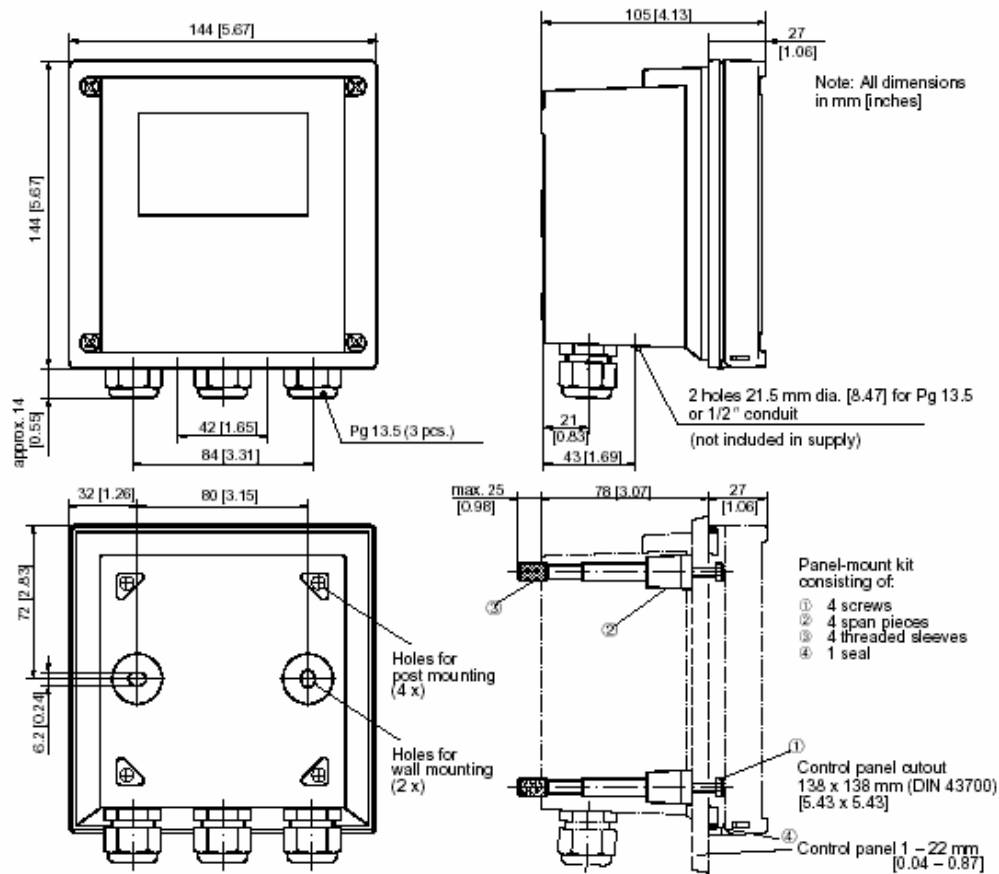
Desenho dimensional do Transmissor, diagrama da montagem e kit de montagem do painel ZU 0275.
